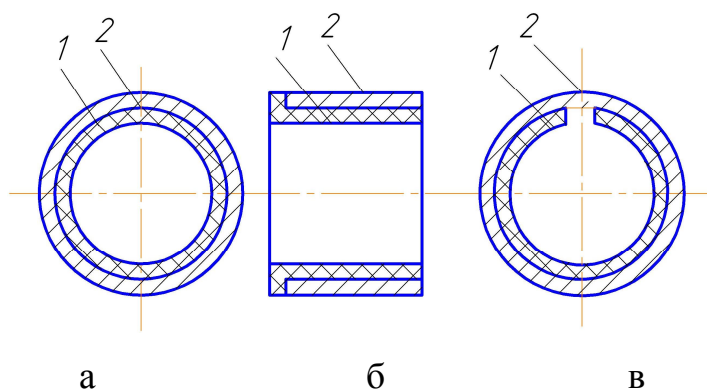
Схемы крепления полимерных втулок в корпусе подшипника скольжения: 1 - втулка; 2 – корпус.
